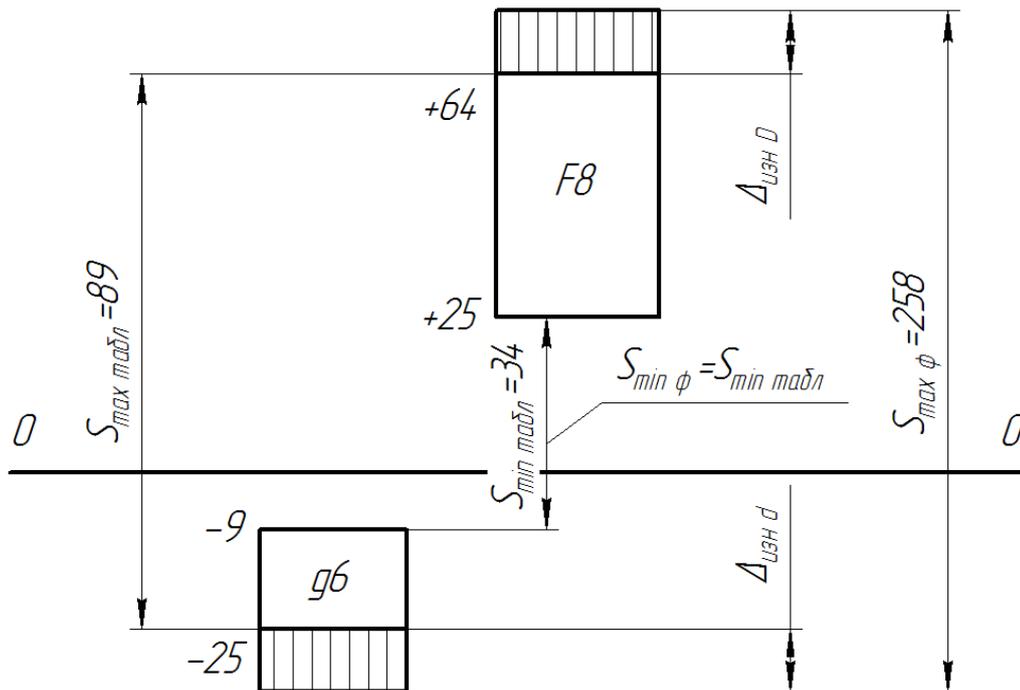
Схема полей допусков посадки с зазором
